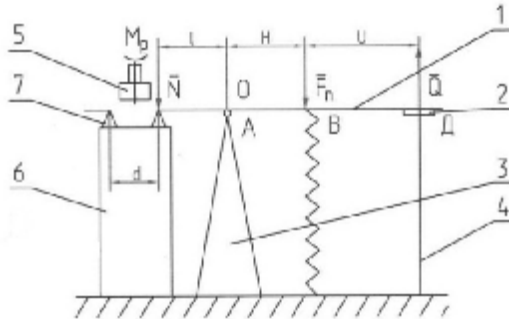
Схема приспособления: 1 – рычаг; 2 – гайка; 3 – стойка;
